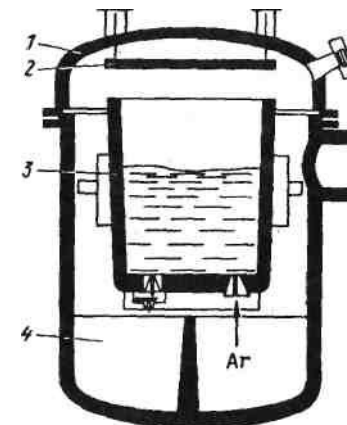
Установка вакуумирования стали в ковше: 1 — вакуум-крышка; 2 — теплозащитный экран; 3 — сталеразливочный ковш; 4 — вакуум-камера
